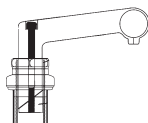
Конструкция резьбовой рулевой колонки и регулировка положения руля
